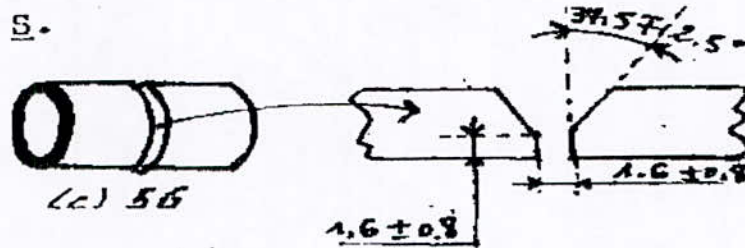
Préparation des joints en vue de soudage
